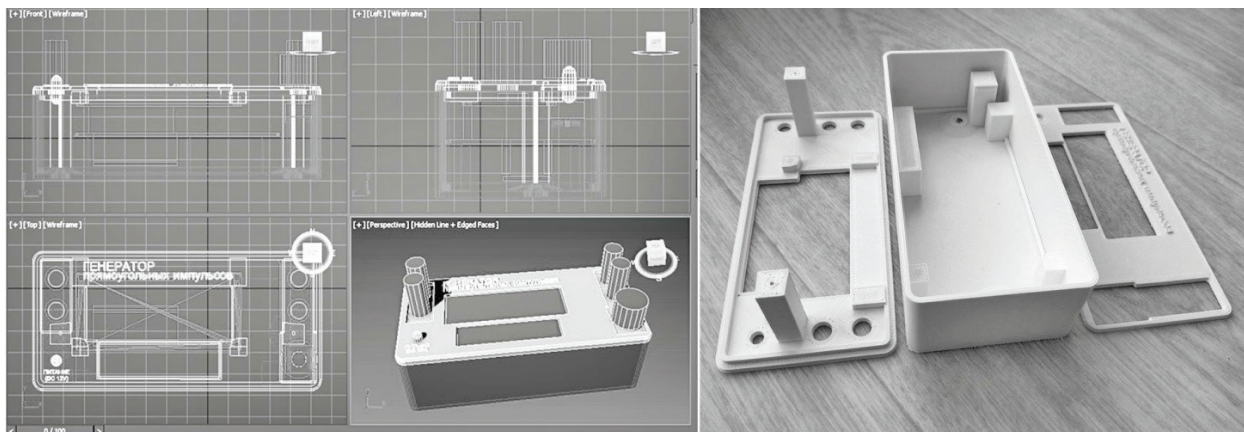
Трехмерная модель в 3D-Max и распечатанный корпус
